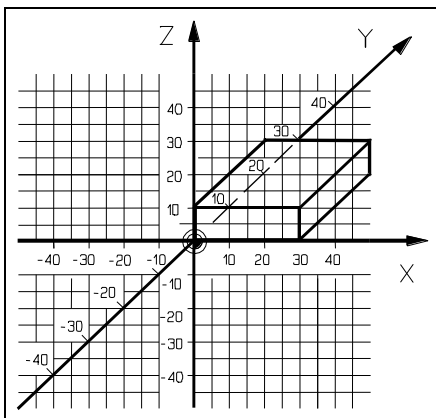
Розташування нульової точки заготовки при роботі на фрезерному верстаті з ЧПК
